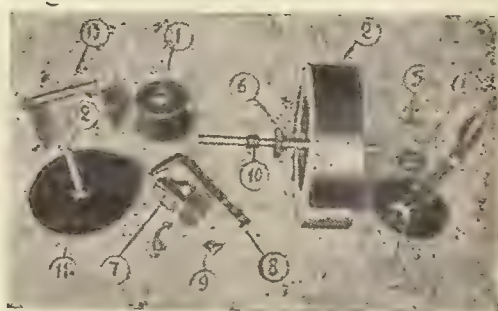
Детали установки т. Успенского: 1 — барабан для записи; 2 — маховик; 3 и 4 — шестерни зубчатого механизма; 5 — нит крепления большой шестерни; 6 — червячная шестерня центробежного регулятора; 7 — центробежный регулятор; 8 — стойка крепления центробежного регулятора; 9 — подпятник центробежного регулятора; 10 — резиновое кольцо фрикционного перебора механизма смещения рекордера; 11 и 12 — фрикционный диск и нит смещения рекордера; 13 — кронштейн крепления винта смещения
